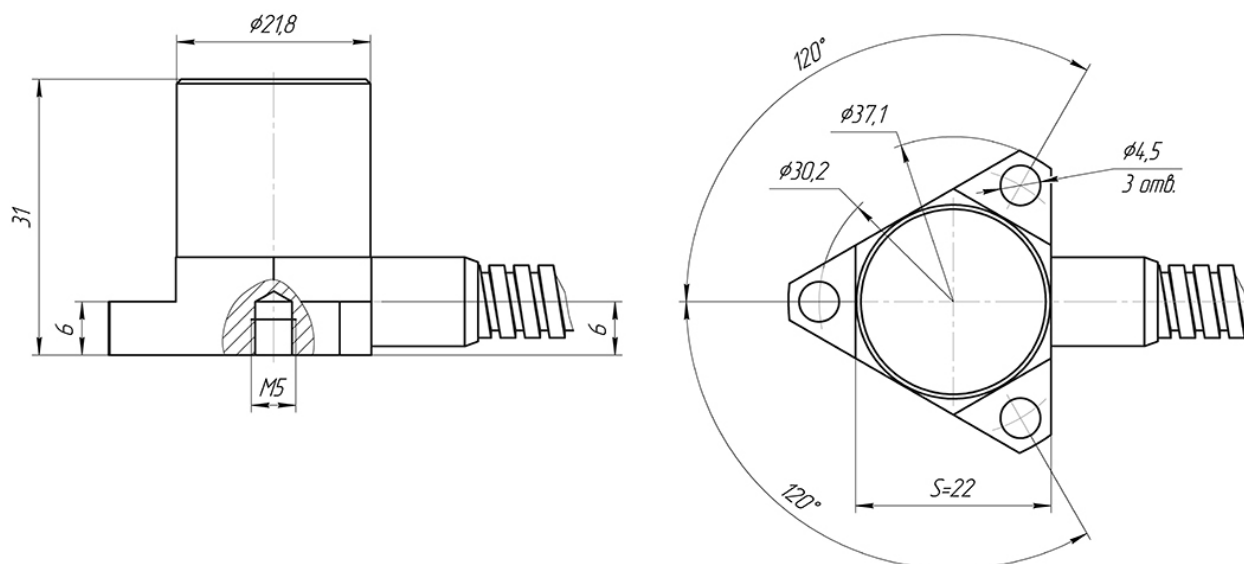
Габаритный чертеж акселерометра ZET 112
